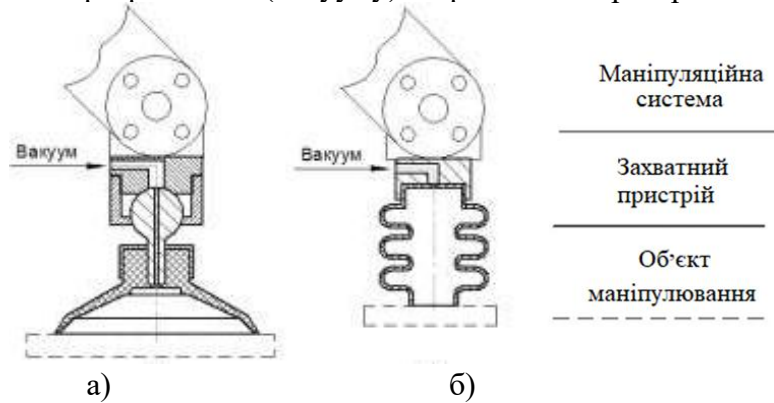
Принципова схема дії вакуумного захватного пристрою
